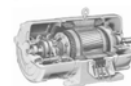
Despiece de un motor de inducción de rotor devanado
